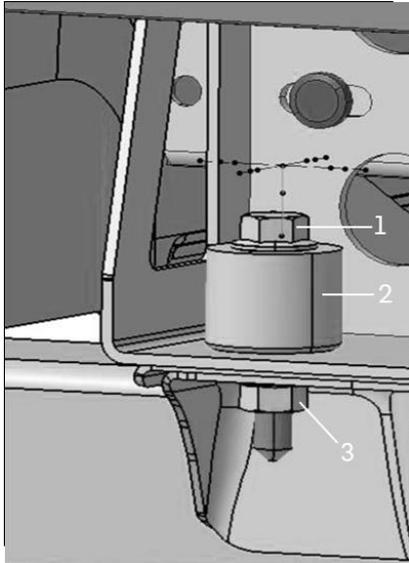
exemple de conception : assemblage vissé avec élément amortisseur (schéma de principe)
